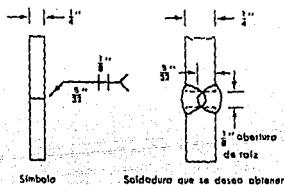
Símbolo de soldadura de acanaladura cuadrada y soldadura que se desea obtener.
